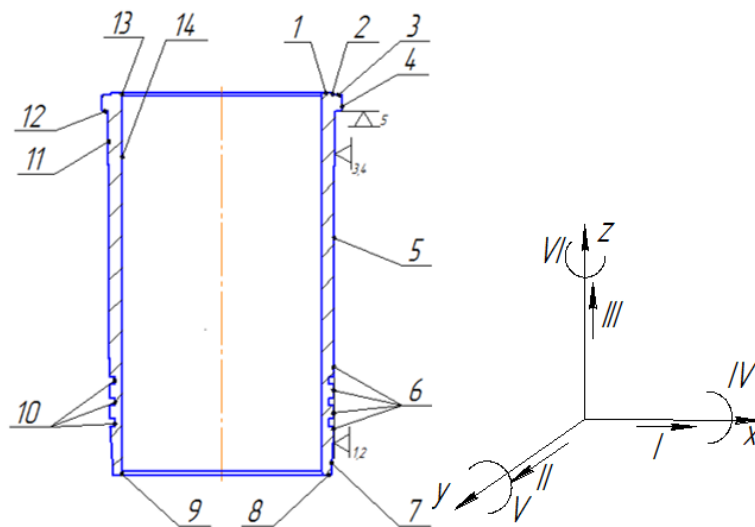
Ескіз гільзи циліндра з класифікацією поверхонь
